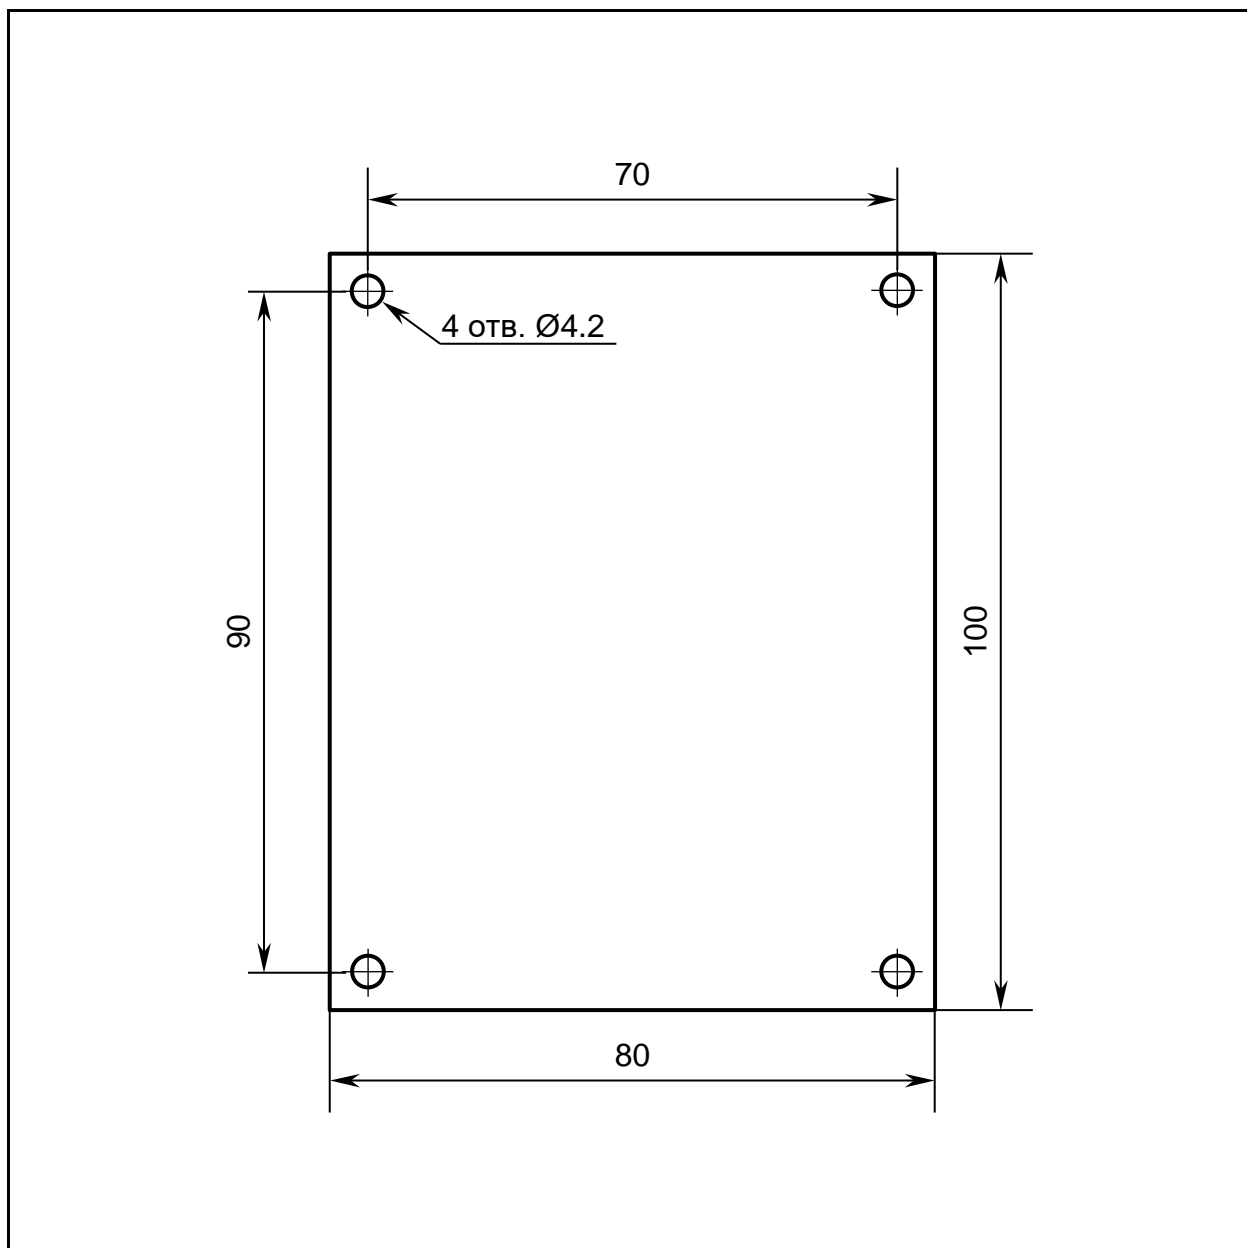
Габаритные размеры модуля и расположение крепежных отверстий
